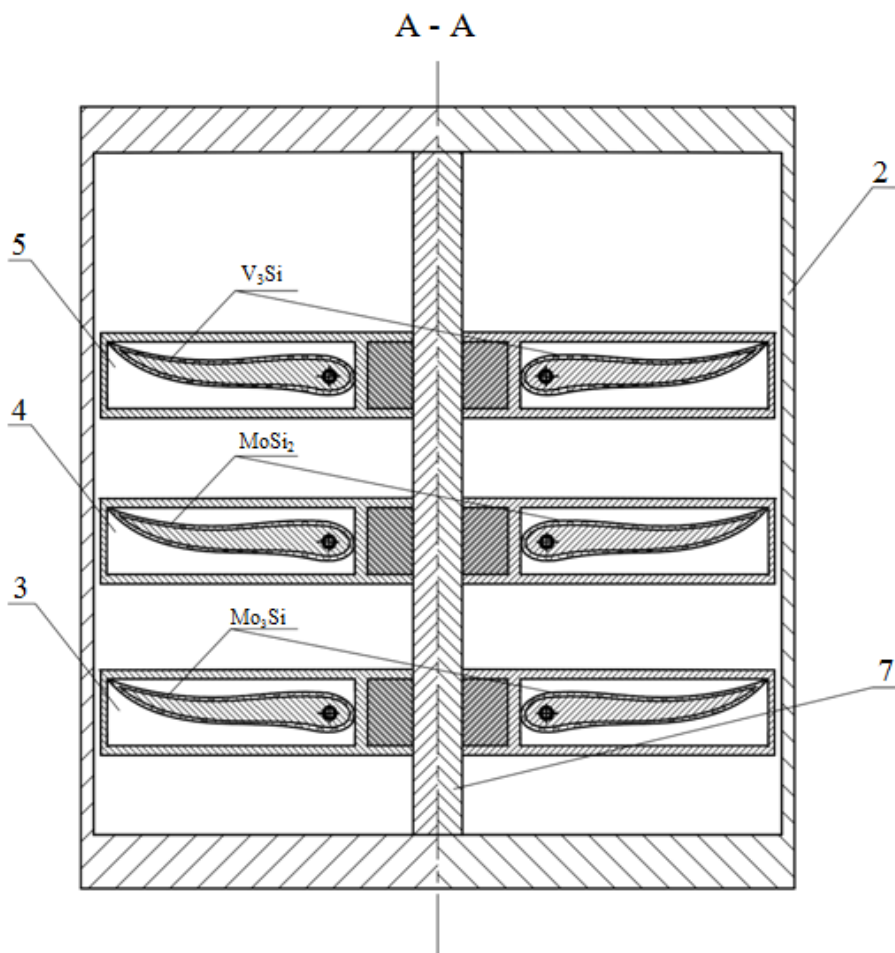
Продольный разрез рабочих колес динамического каталитического дожигателя
